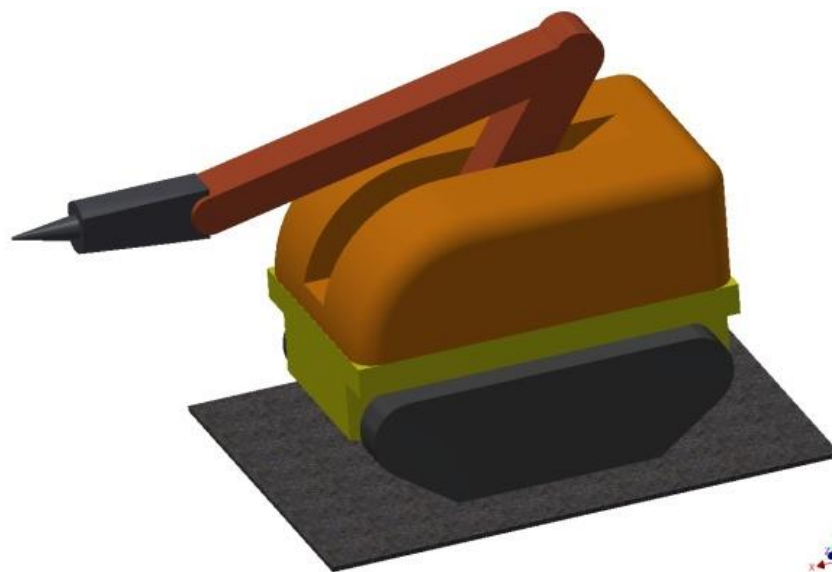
Внешний вид РТК аварийно-спасательного назначения
